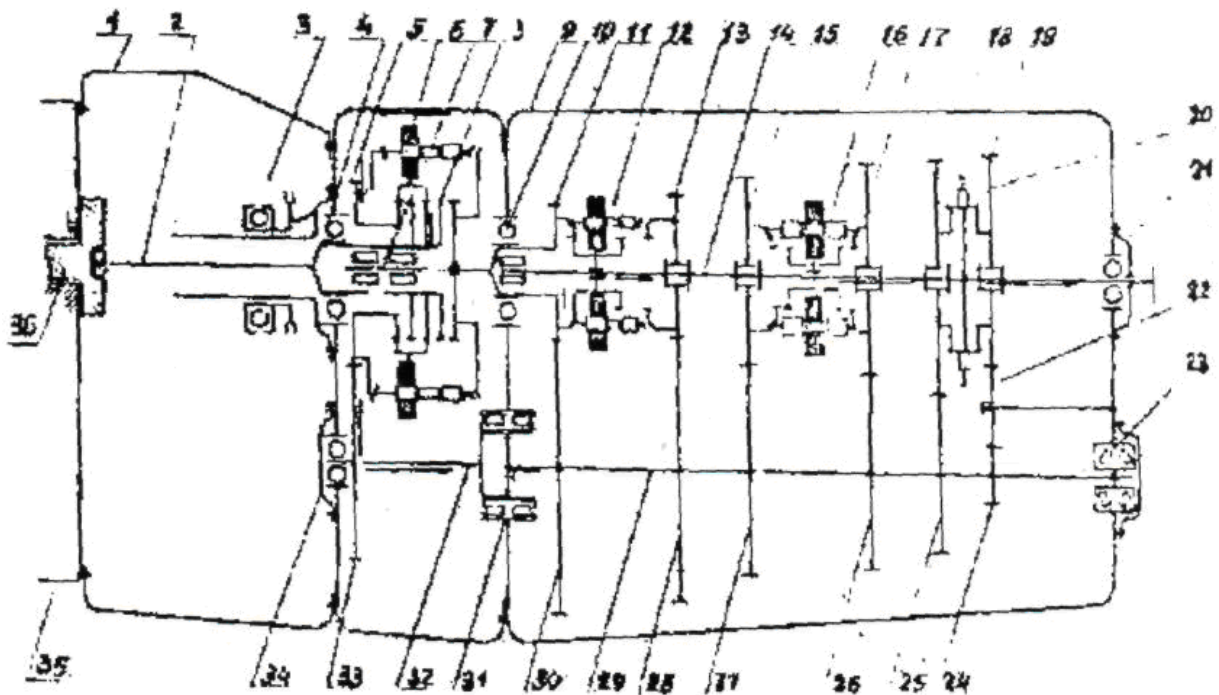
Кінематична схема тривальної коробки передач з дільником:
